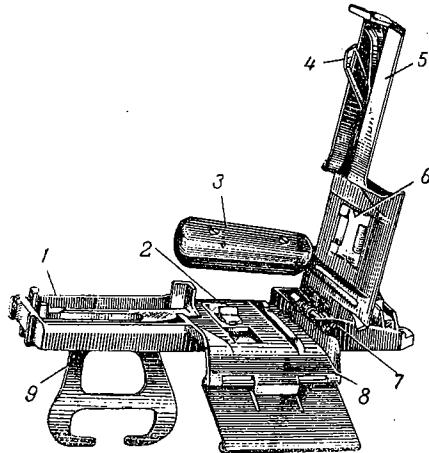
Приемник с открытой крышкой, подготовленный для разборки:
